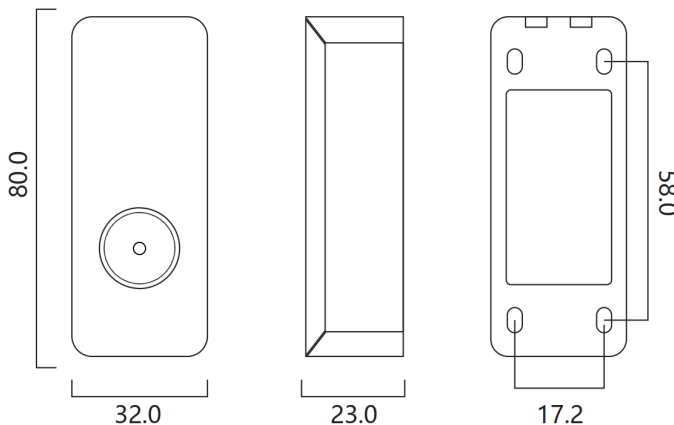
Считыватель QR-485-3 (накладной). Габариты изделия.
